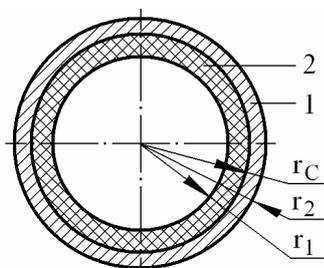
Схема поперечного сечения цилиндрической отливки с полым стержнем:
